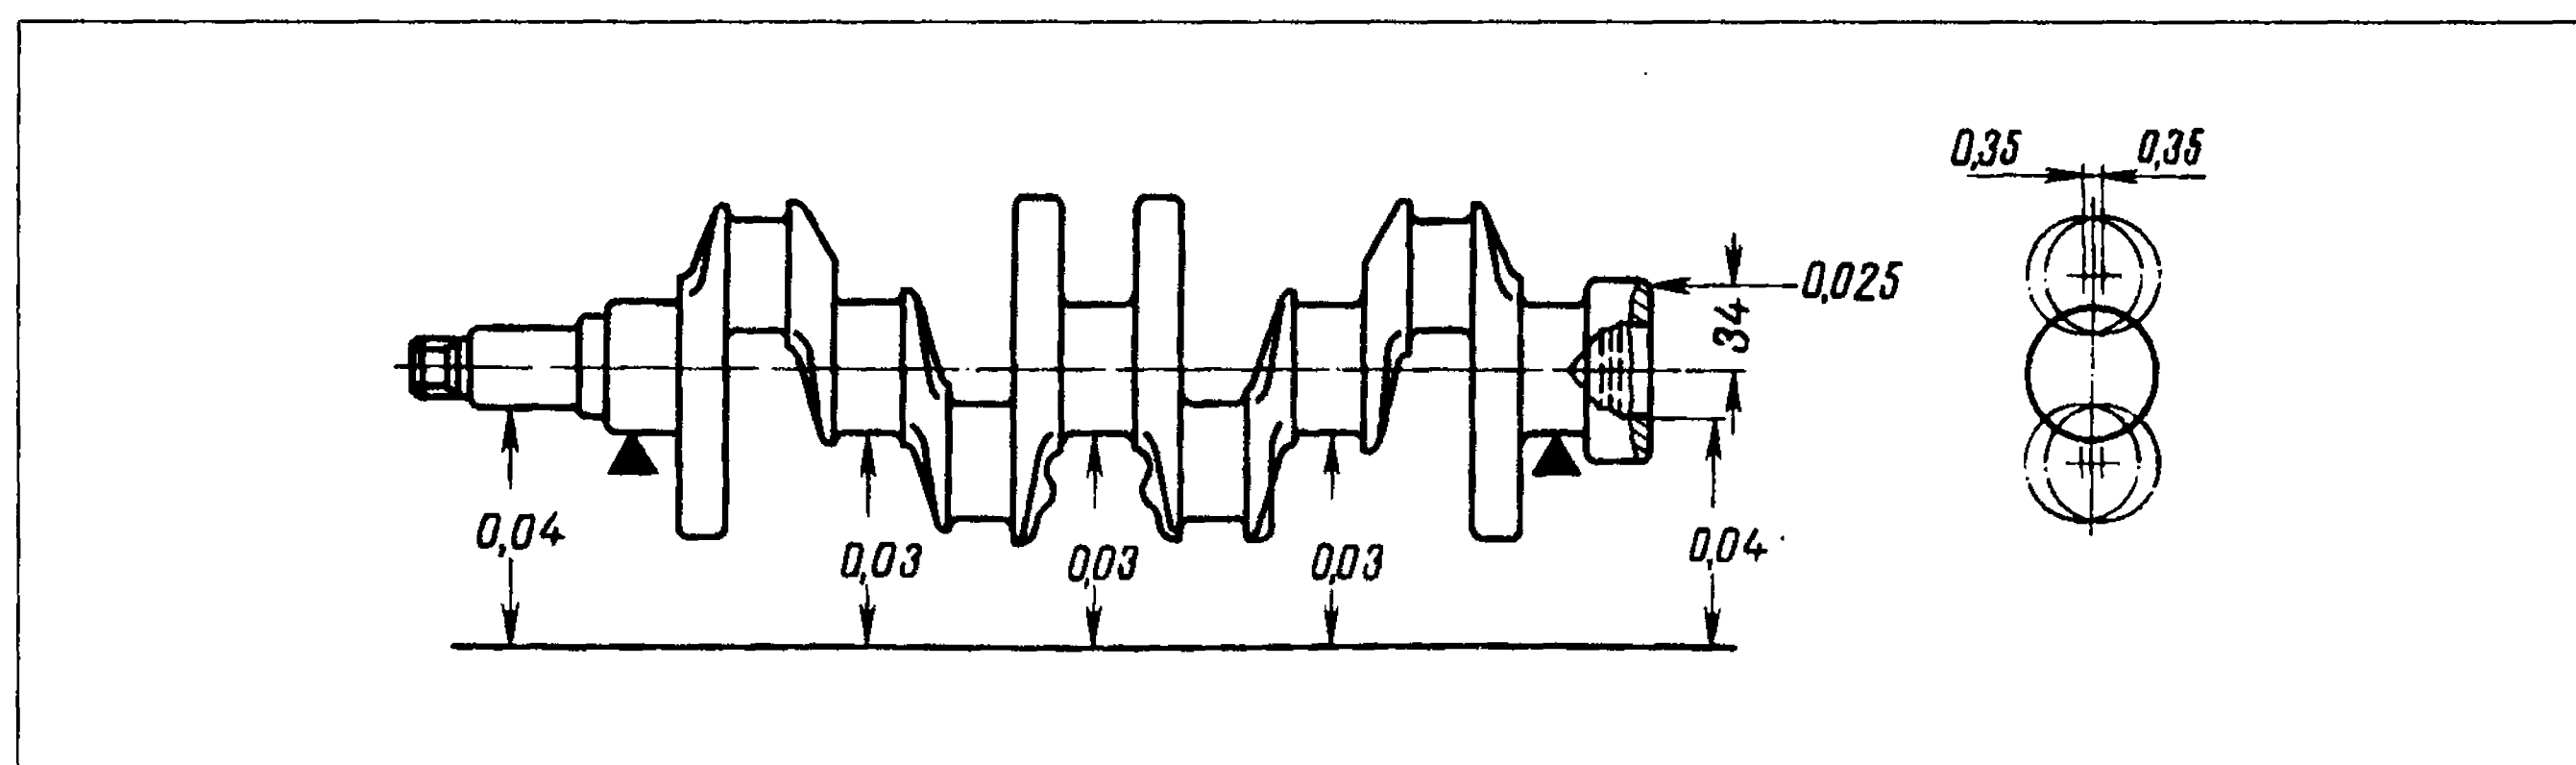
Допустимые биения основных поверхностей коленчатого вала
